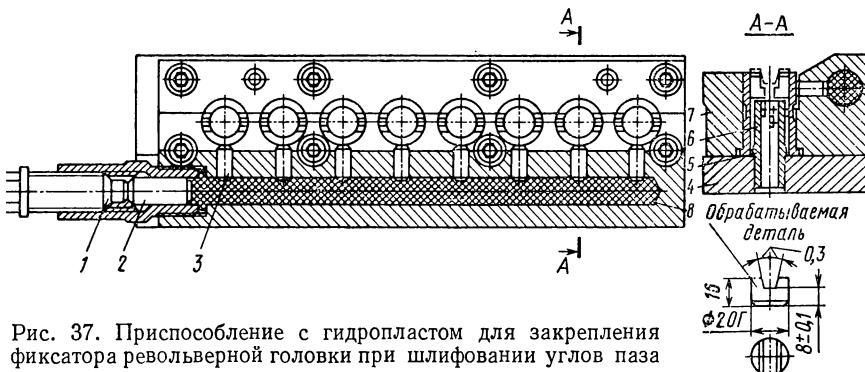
Приспособление с гидропластом для закрепления фиксатора револьверной головки при шлифовании углов паза
